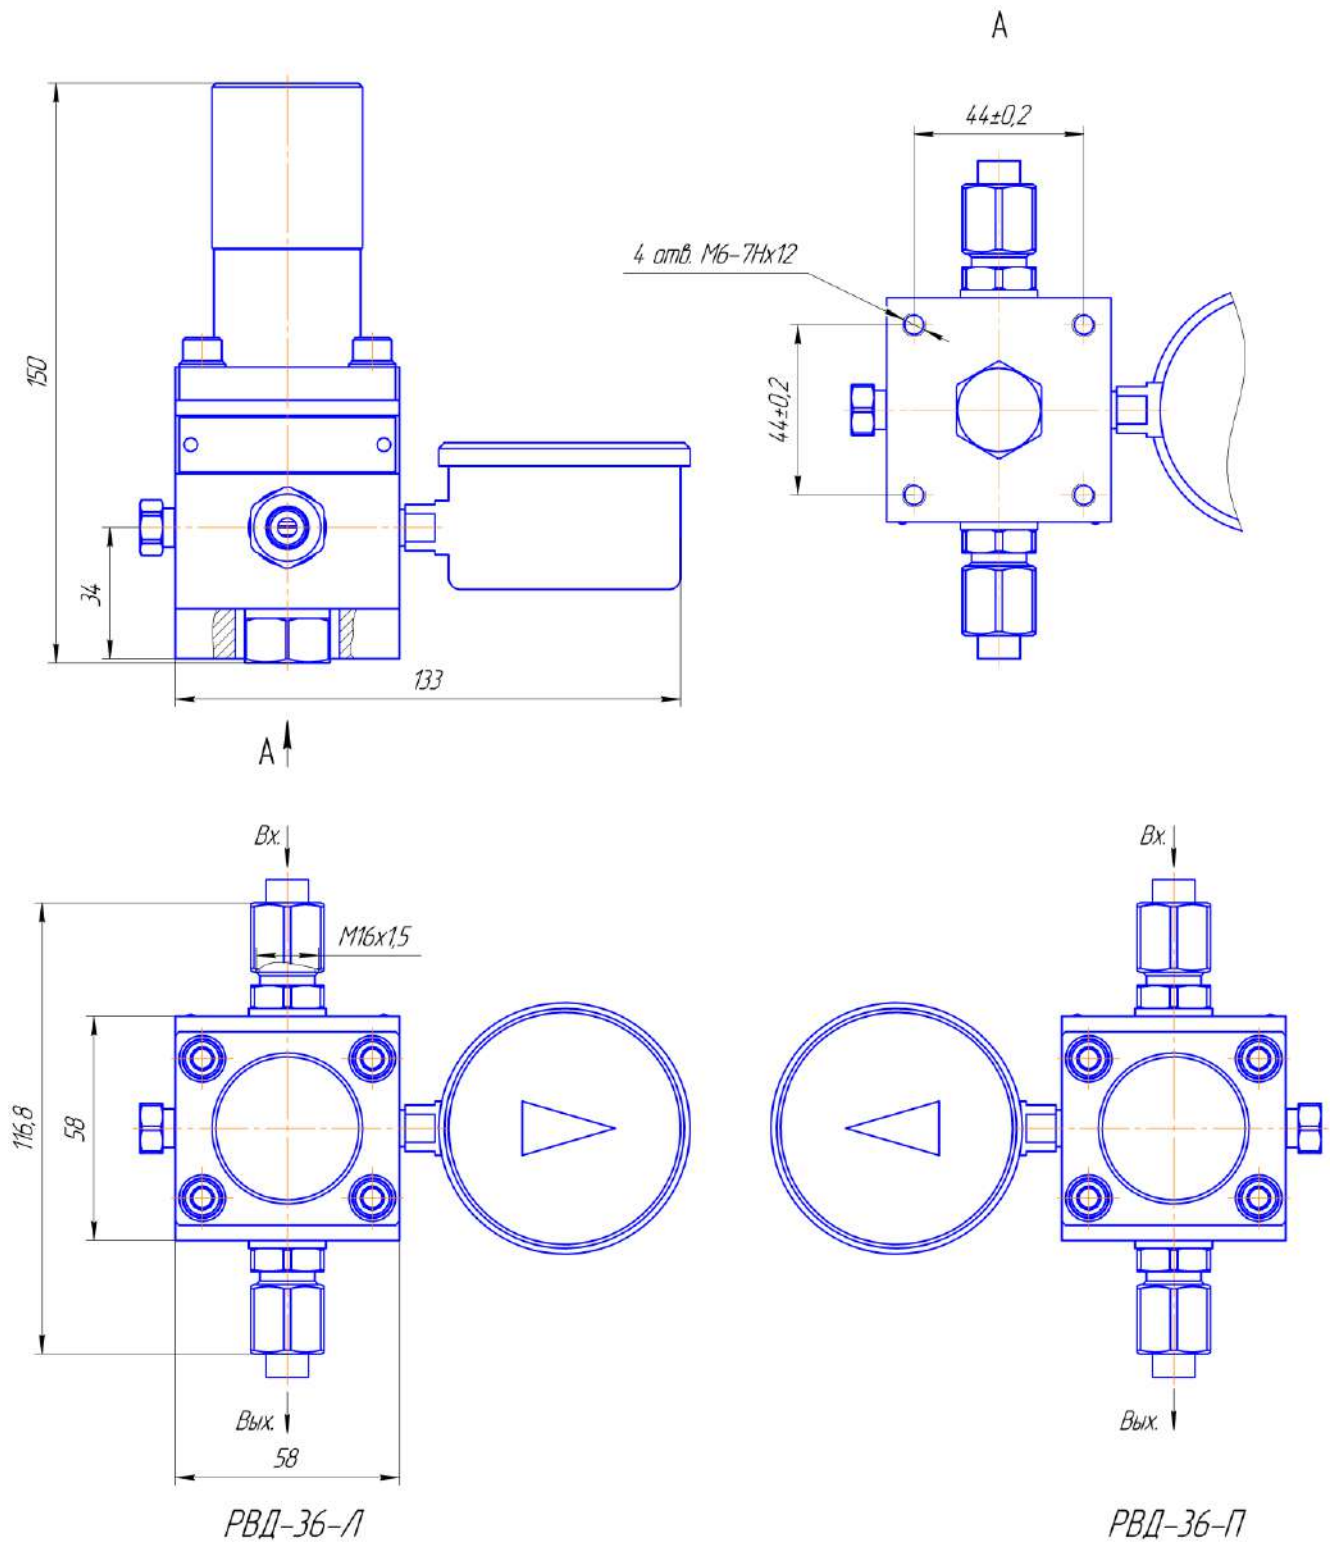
Габаритные и присоединительные размеры редуктора РВД-36
